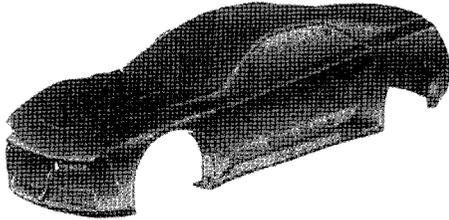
Reverse engineering에 의한 CAD 모델 구축 예
